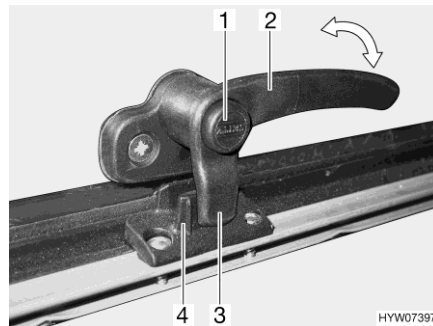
Leva di serraggio con bottone di sicurezza in posizione "Chiuso"
